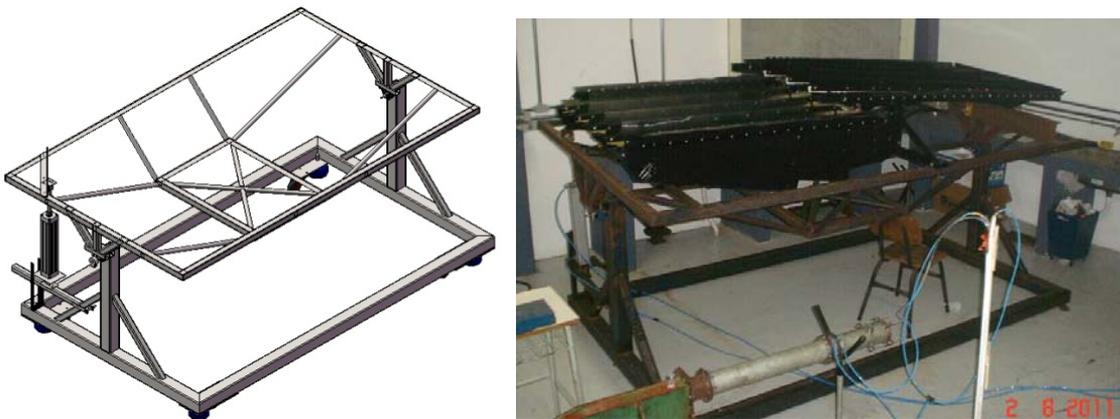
Vista tridimensional do projeto da bancada ao lado da foto do protótipo construído.
